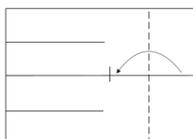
Определение линии будущего контура крыла: разметка заготовки в верхней части листа
